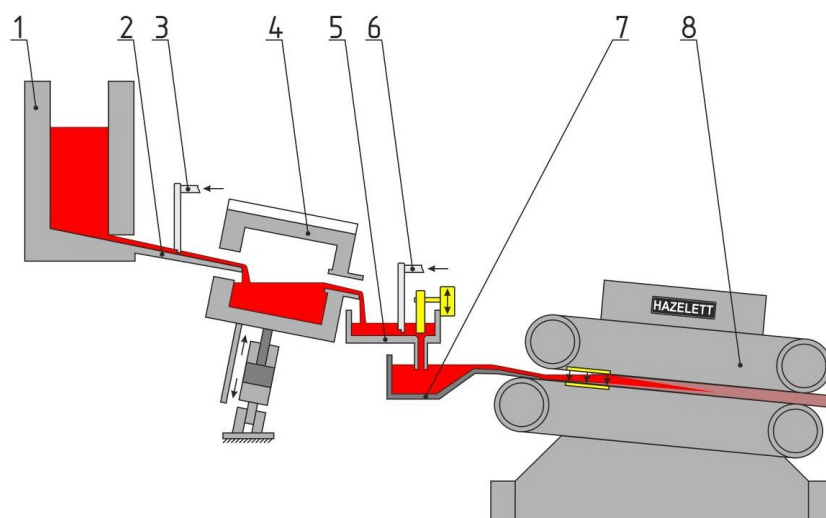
Схема плавно-литейного участка линии Contirod (1 – шахтная газовая печь; 2 – соединительный желоб; 3 – трубка для вдувания воздуха; 4 – печь-миксер; 5 – литейный желоб; 6 – трубка для подачи азота; 7 – промежуточный ковш; 8 – литейная машина)
